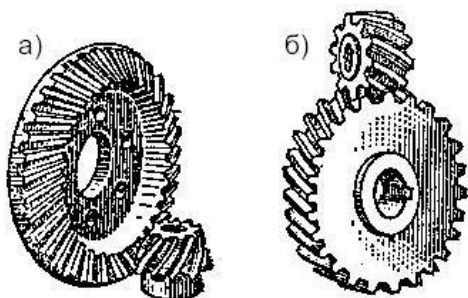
Зубчаті колеса з осями, що перехрещуються:
